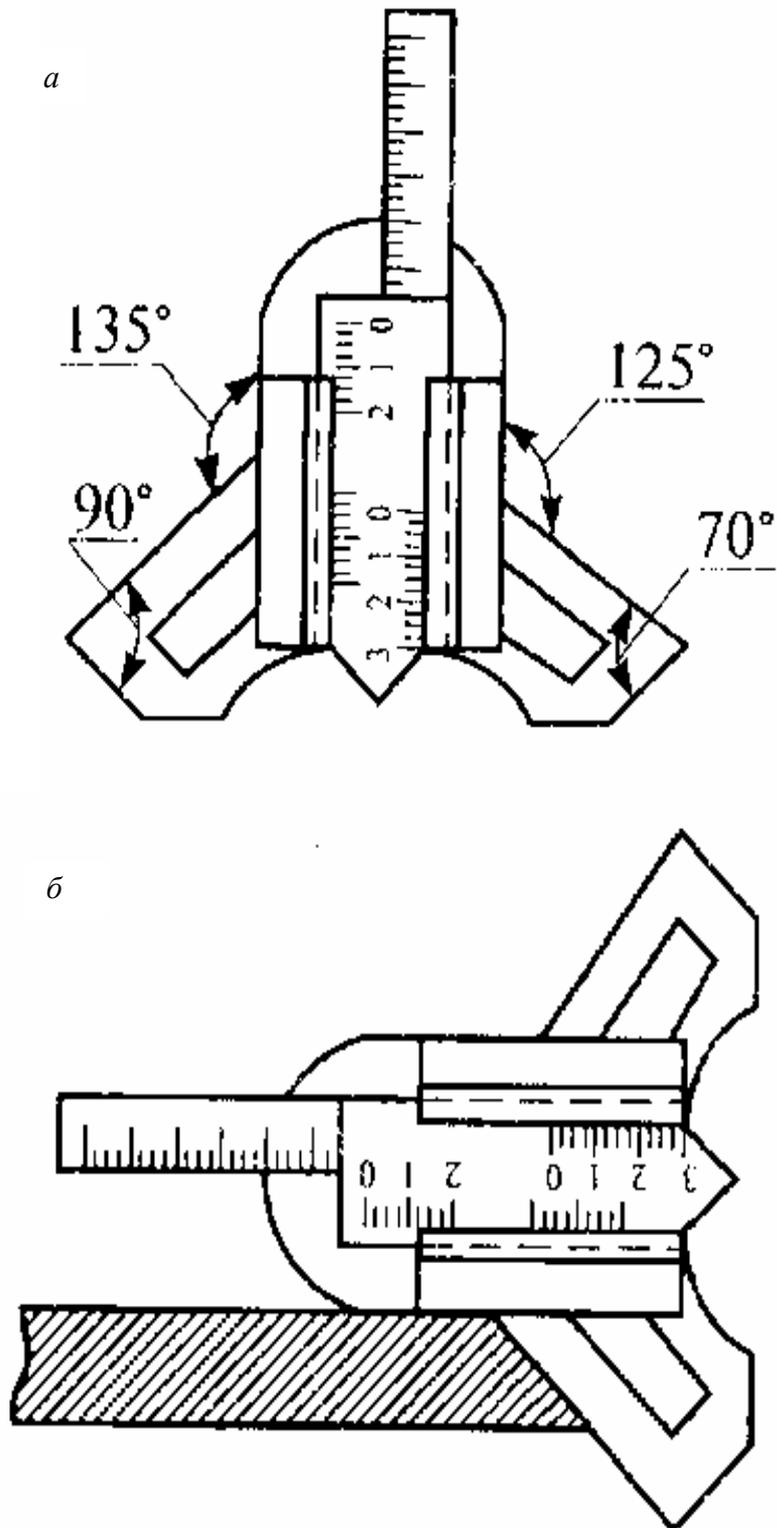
Контроль сварных швов шаблоном конструкции В.Э. Ушера-Маршака:
